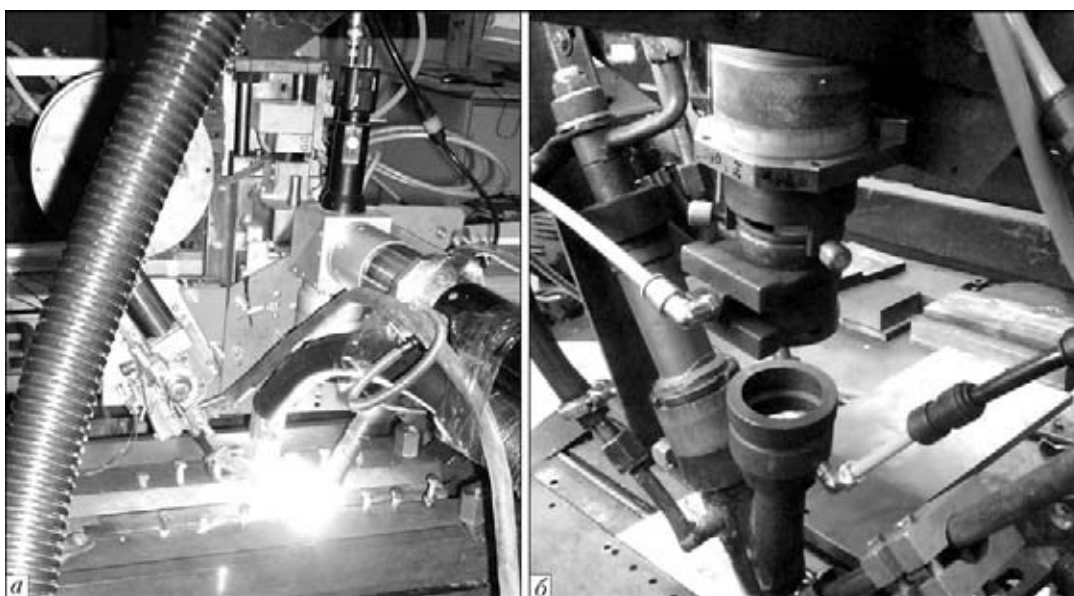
Оборудование для лазерной (а) и лазерно-дуговой сварки (б) стали ХГС толщиной 3, 6 и 10 мм с использованием присадочной проволоки Св-18ХМА диаметром 1,2 мм и различных защитных газов
